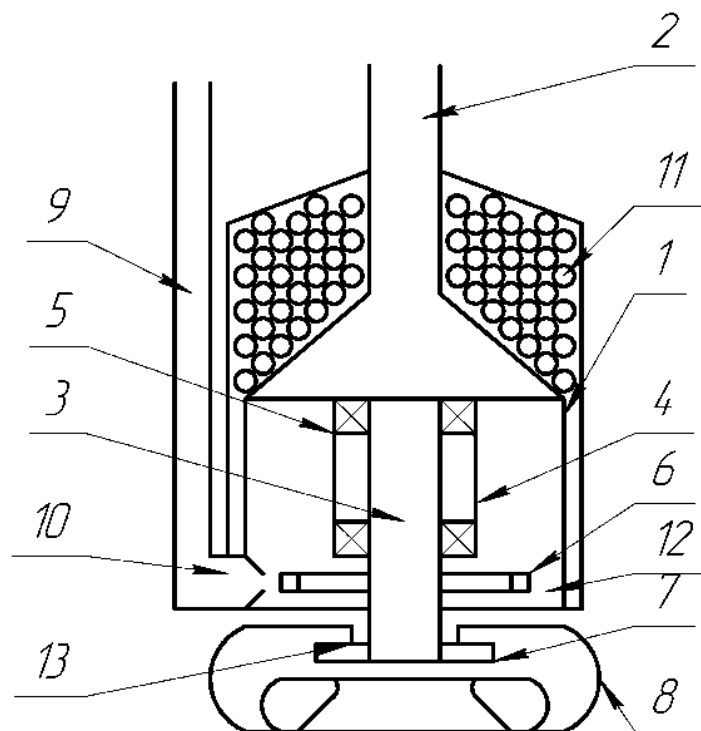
Ерліфтна установка з вихроутворювачем: 1 – корпус-змішувач; 2 – підйомний патрубков; 3 – подаюча труба; 4 – стакан; 5 – підшипник; 6 – турбіна; 7 – вихроутворювач; 8 – ґрунтозабірний пристрій; 9 – повітряний трубопровід; 10 – сопловий апарат; 11 – перфорований кожух; 12 – камера живлення; 13 – канал
